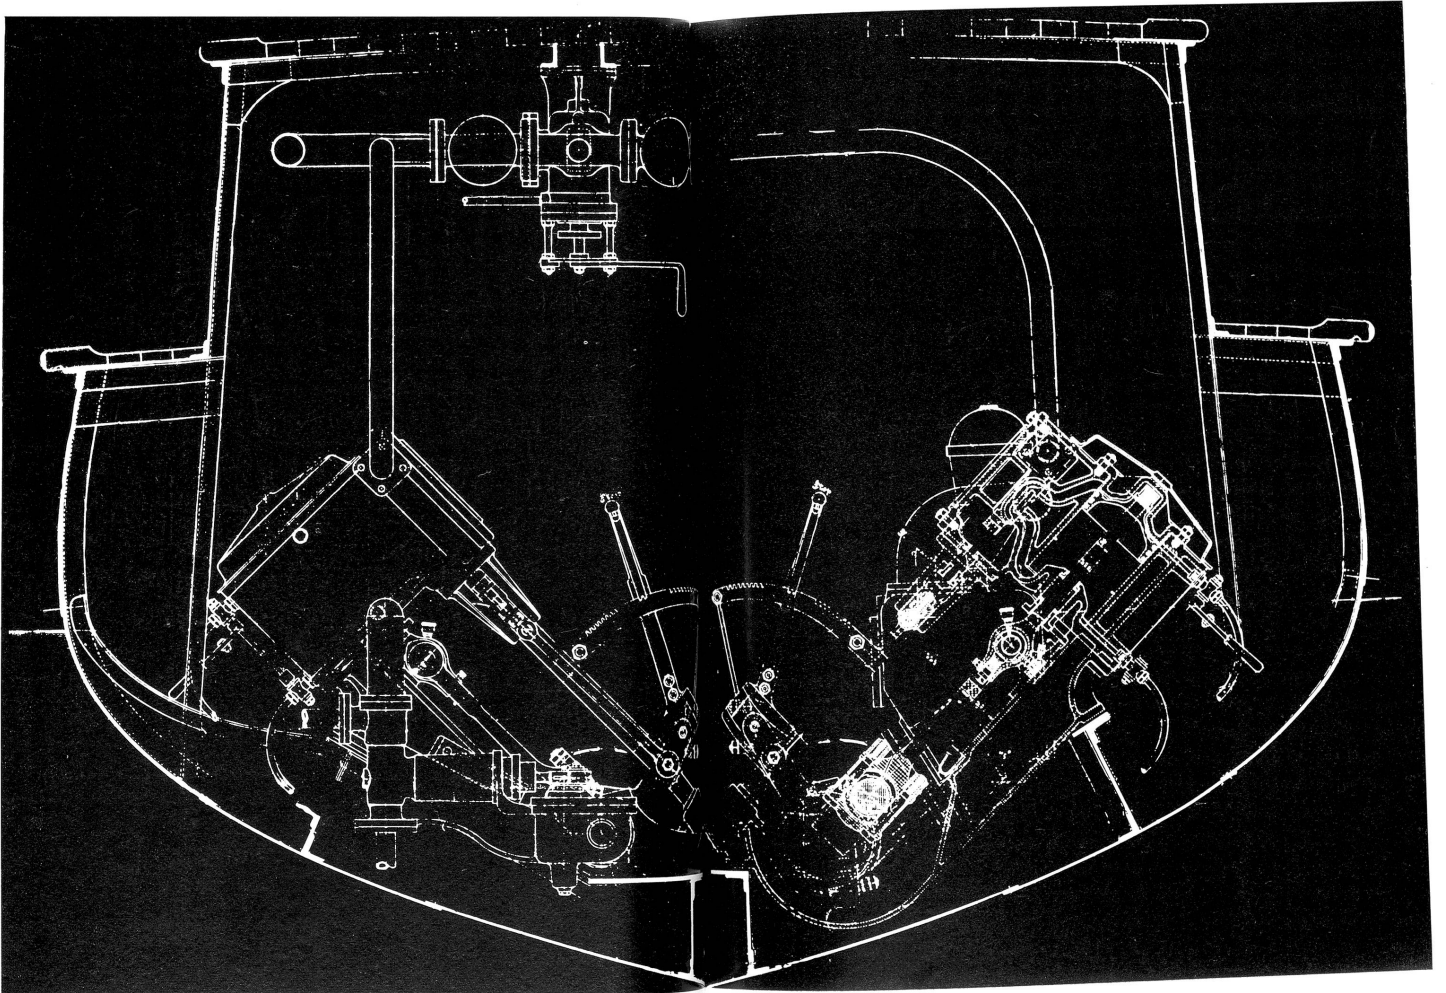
Maschinenanlage. Aufriss. Von vorn gesehen. Zeichnung Gebr. Sulzer, Winterthur, 1891)
